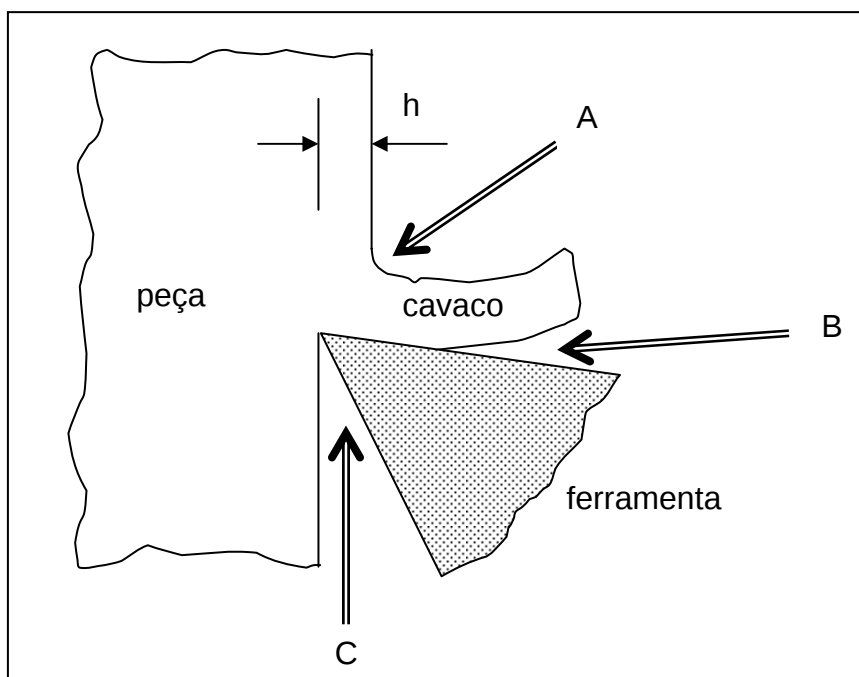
Possíveis direções de aplicação de fluido de corte (Machado & Silva,1999).
